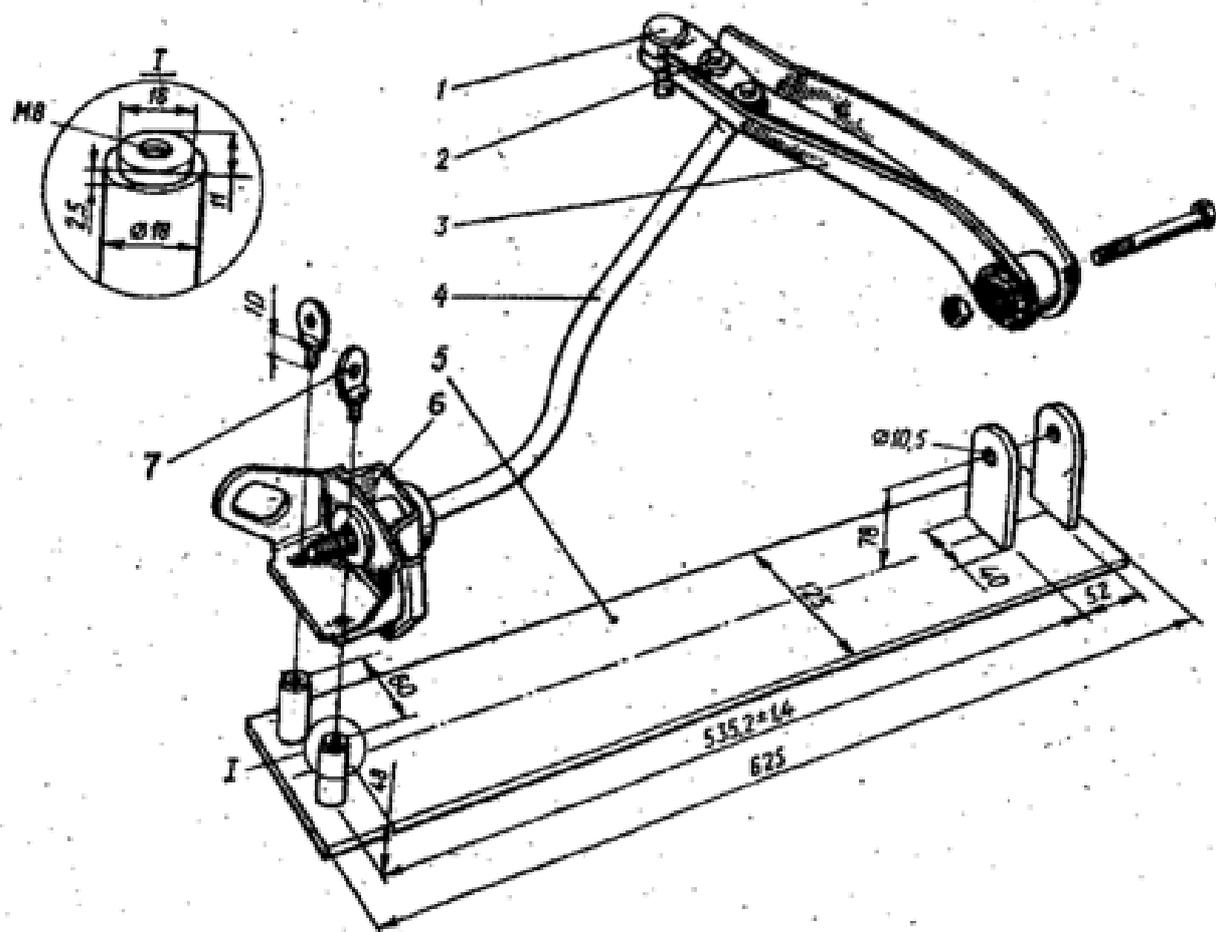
Предварительная сборка в приспособлении рычага передней подвески с реактивной штангой: 1 - шарнир шаровой; 2 - гайка крепления штанги и шарового шарнира к рычагу; 3 - рычаг с сайлентблоком в сборе; 4 - штанга реактивная; 5 - приспособление для сборки; 6 - хронштейн с сайлентблоком в сборе; 7 - гайка
